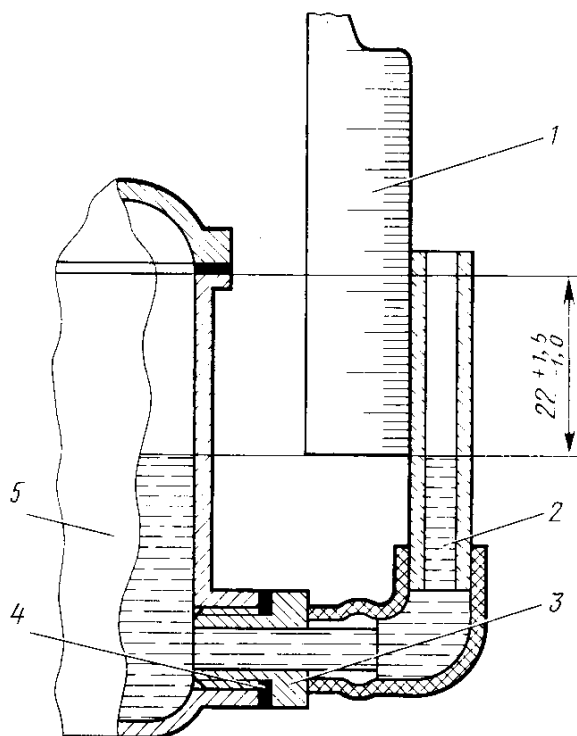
Приспособление для проверки уровня топлива в поплавковой камере карбюраторов К-133 и К-133А: 1 — масштабная линейка; 2 — стеклянная трубочка; 3 — штуцер; 4 — прокладка; 5 — карбюратор
